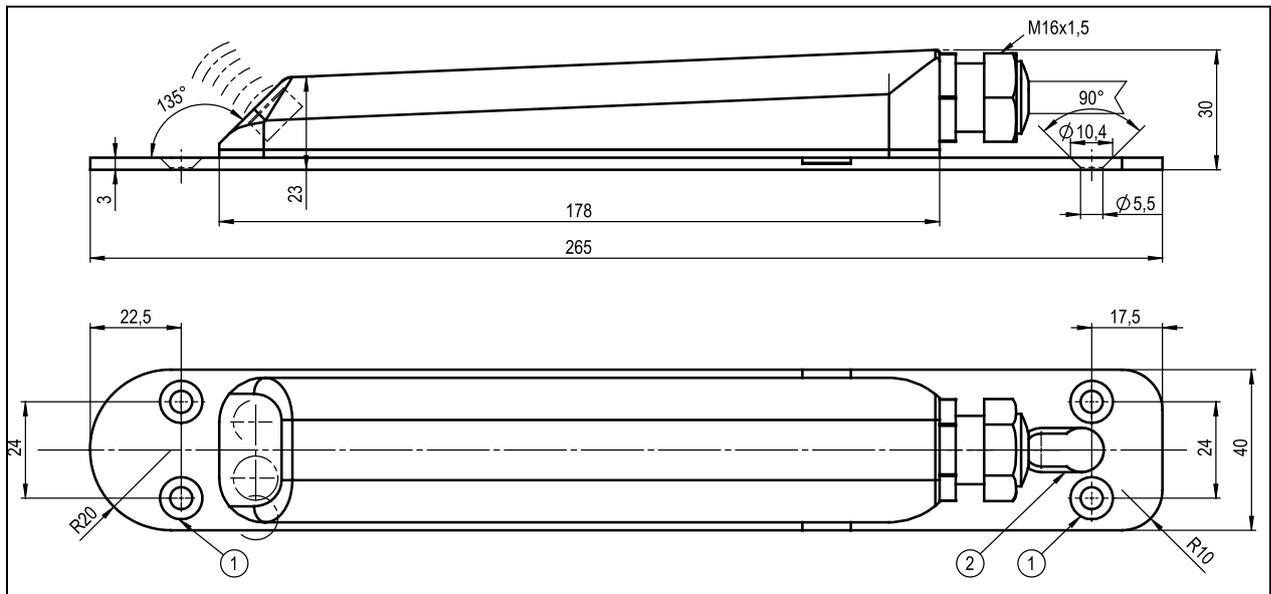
Dimensions boîtier PCM F et connexion capteurs
